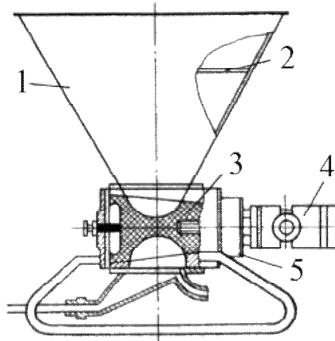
Общий вид зарядной установки типа ЗМБ (УЗС): 1 – бункер; 2 – решетка; 3 – вращающийся барабанный питатель; 4 – пневмодвигатель; 5 – планетарный редуктор
